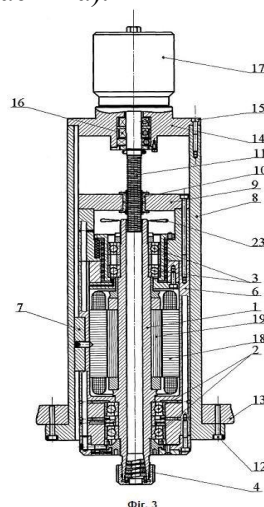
Шпindel 1, передня і задня опори 2 і 3, оправка 4, інструмент 5. піноль 6, шпонка 7, корпус 8. фланець 9, гайка 10, гвинт 11 болти 12 нерухома частина 13, перехідний фланець 14, болти 15, жорстка опора 16 кроковий електродвигун 17, статор 18, двошарова активна поверхня 19
